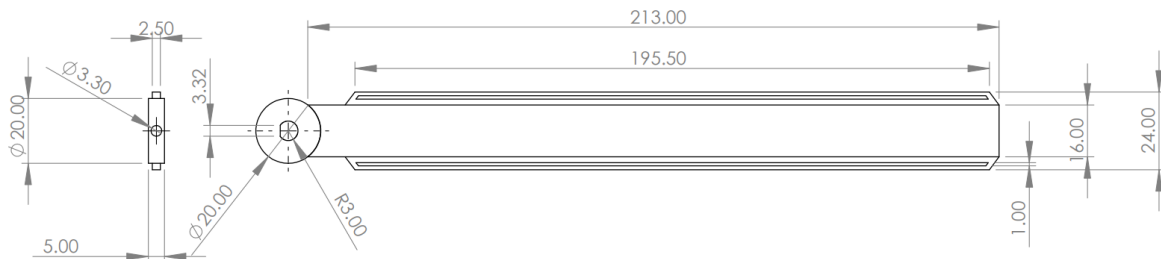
Dimensiones y forma de la pieza móvil diseñada por CAD.
